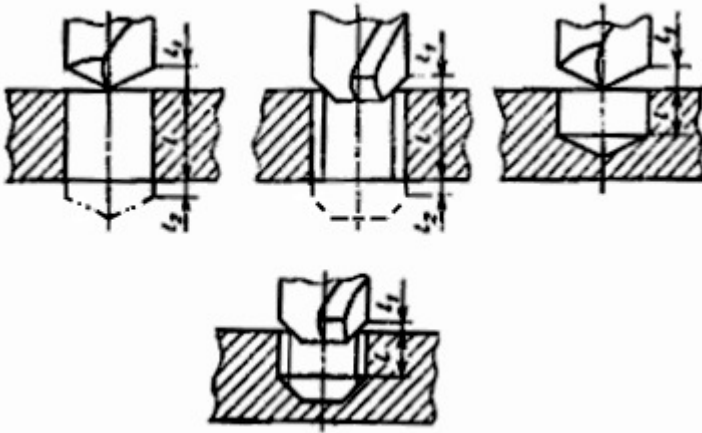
Схеми визначення розрахункової довжини обробки
